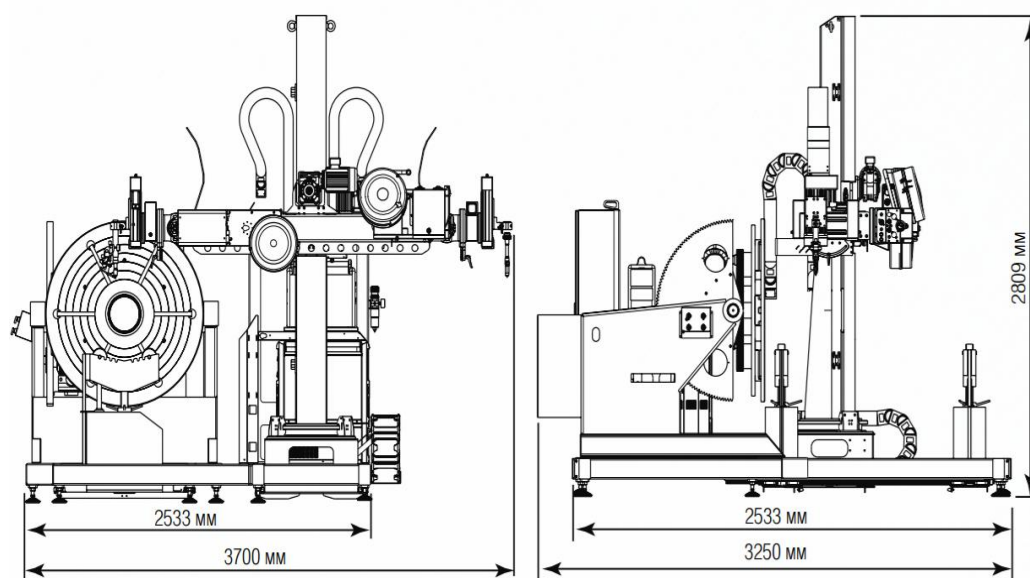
Схема оборудования установки для многопроходной дуговой сварки и наплавки элементов
